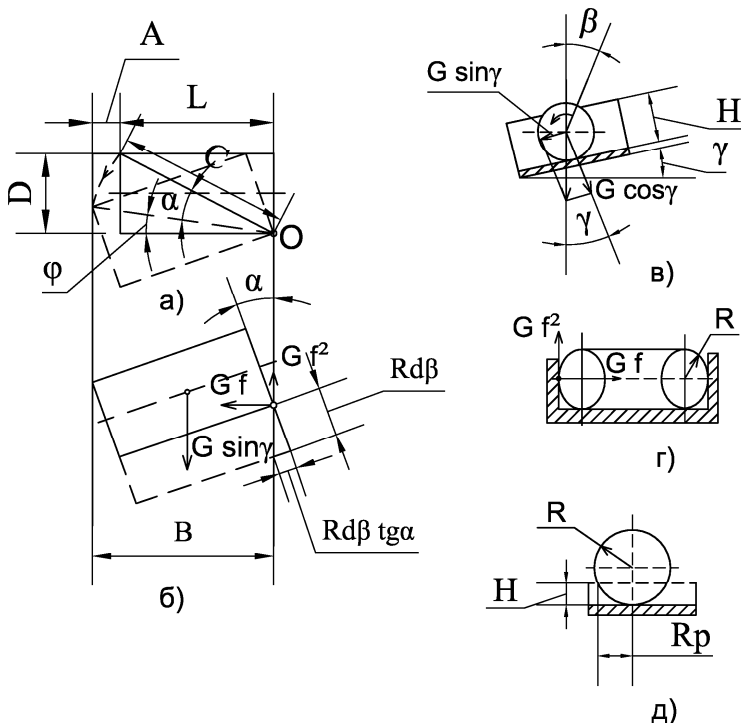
Движение детали в корытовом лотке и схема сил
